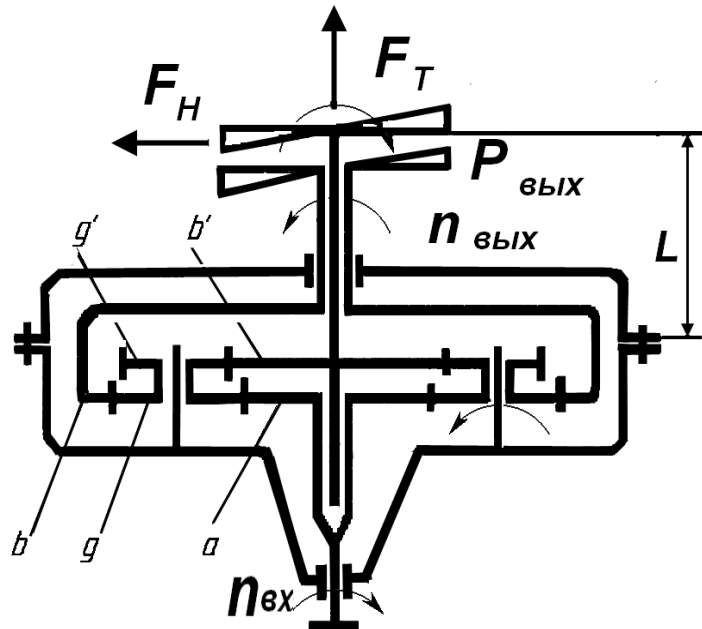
Схема многопоточного редуктора привода соосных винтов вертолета
